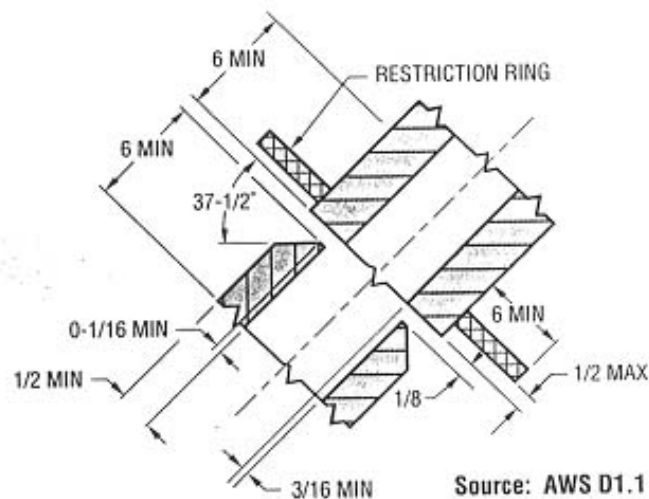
Junta de calificación de soldador AWS D1.1 para conexiones T, K e Y en cañerías o perfiles tubulares.
